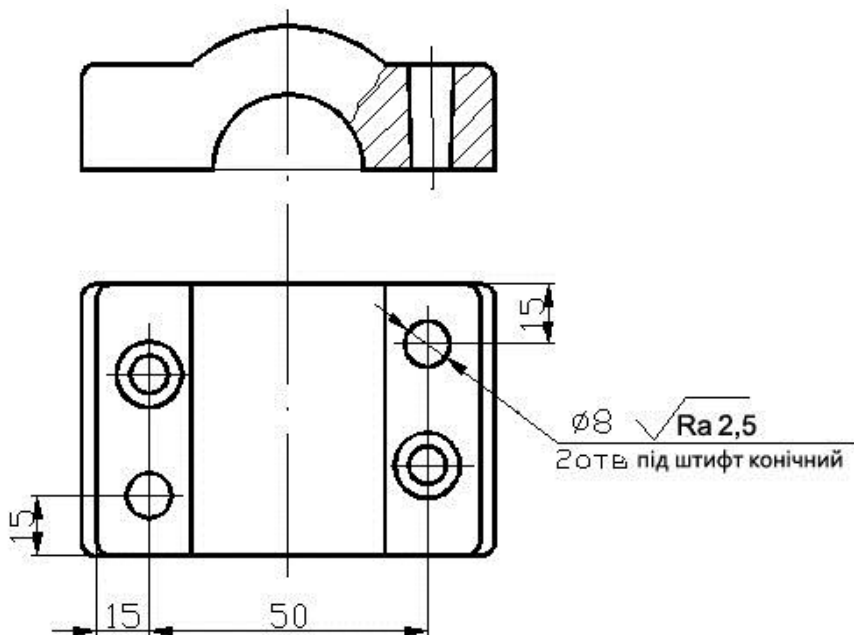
Приклад простановки розмірів при обробці по кондуктору
